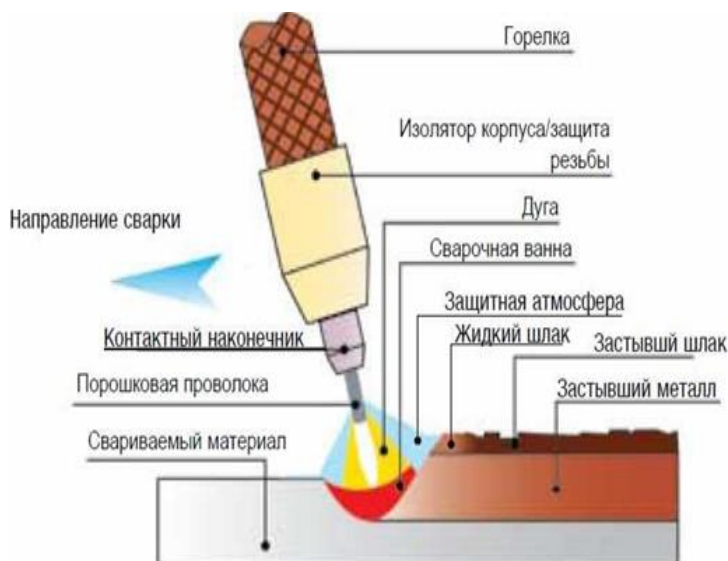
Эскиз механизированной сварки самозащитой порошковой проволокой
